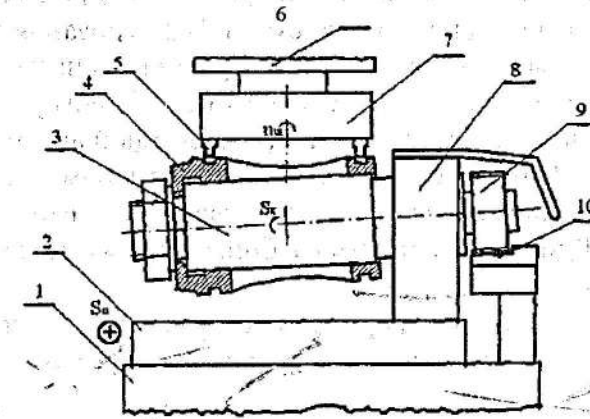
Схема модернизации вертикально-фрезерного станка для нарезания канавки
